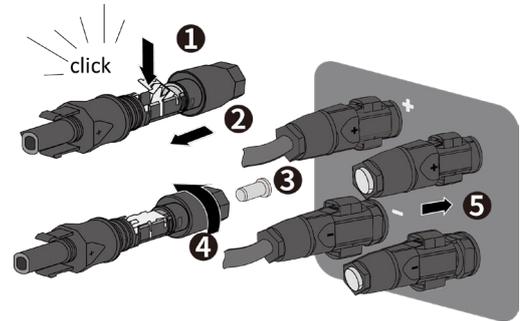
Setzen Sie die DC-Steckverbinder ein und verschließen Sie ungenutzte Steckverbinder
